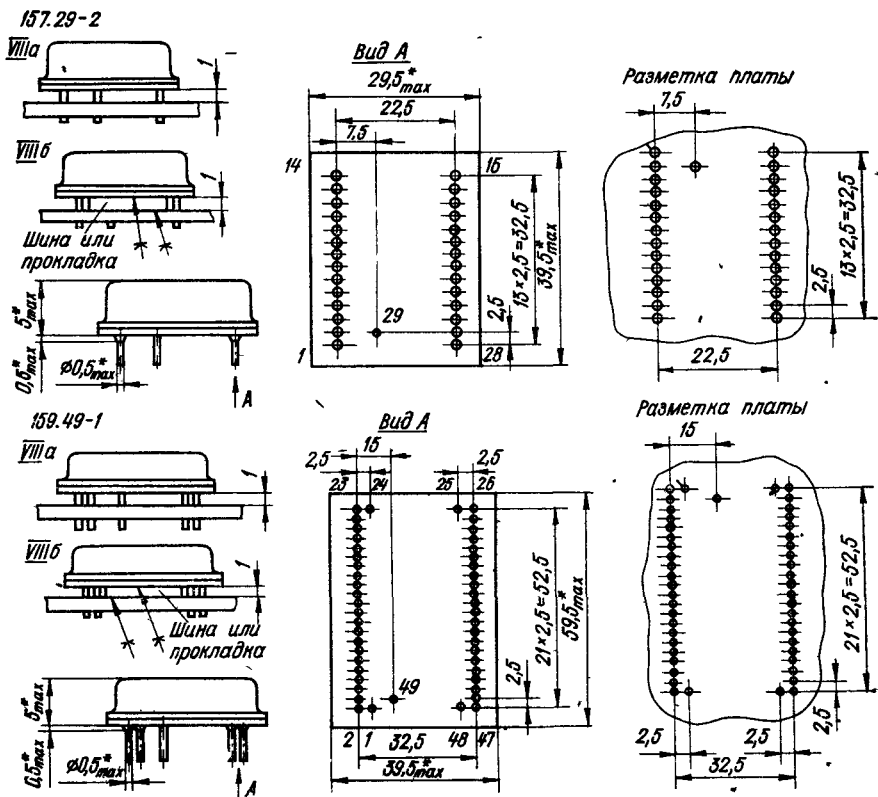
Габаритные и установочные размеры и варианты установки микросхем в корпусе типа 1 (× обозначены размеры для справок)
